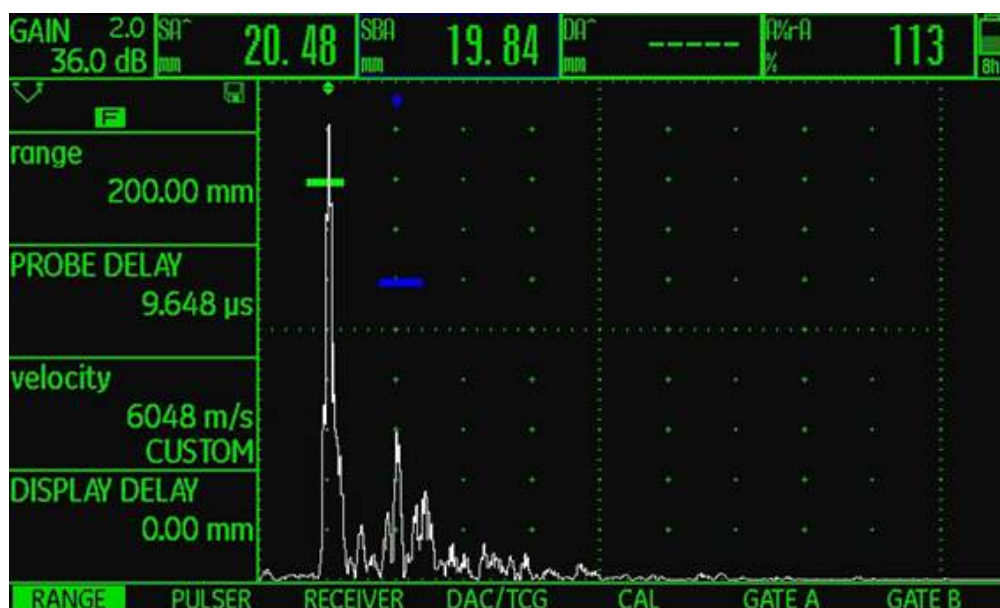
Sinal obtido quando a inspeção com técnicas de ultrassons do provete L-02-5.
